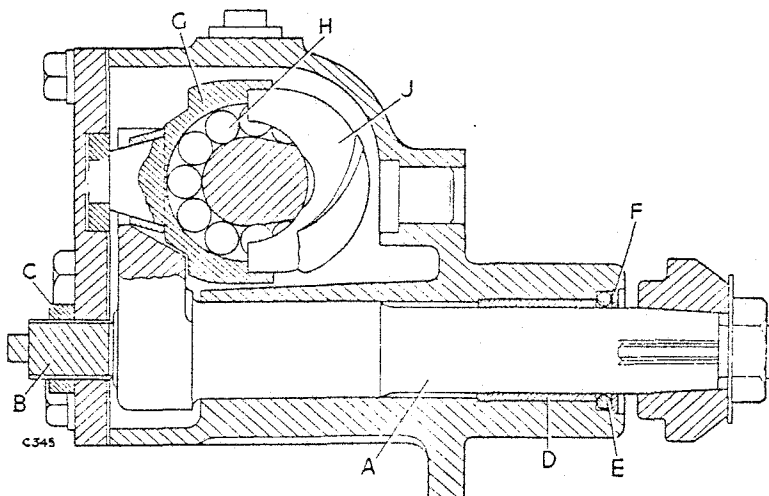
Posiciones relativas de la leva, de los cojinetes y de la tuerca principal.
